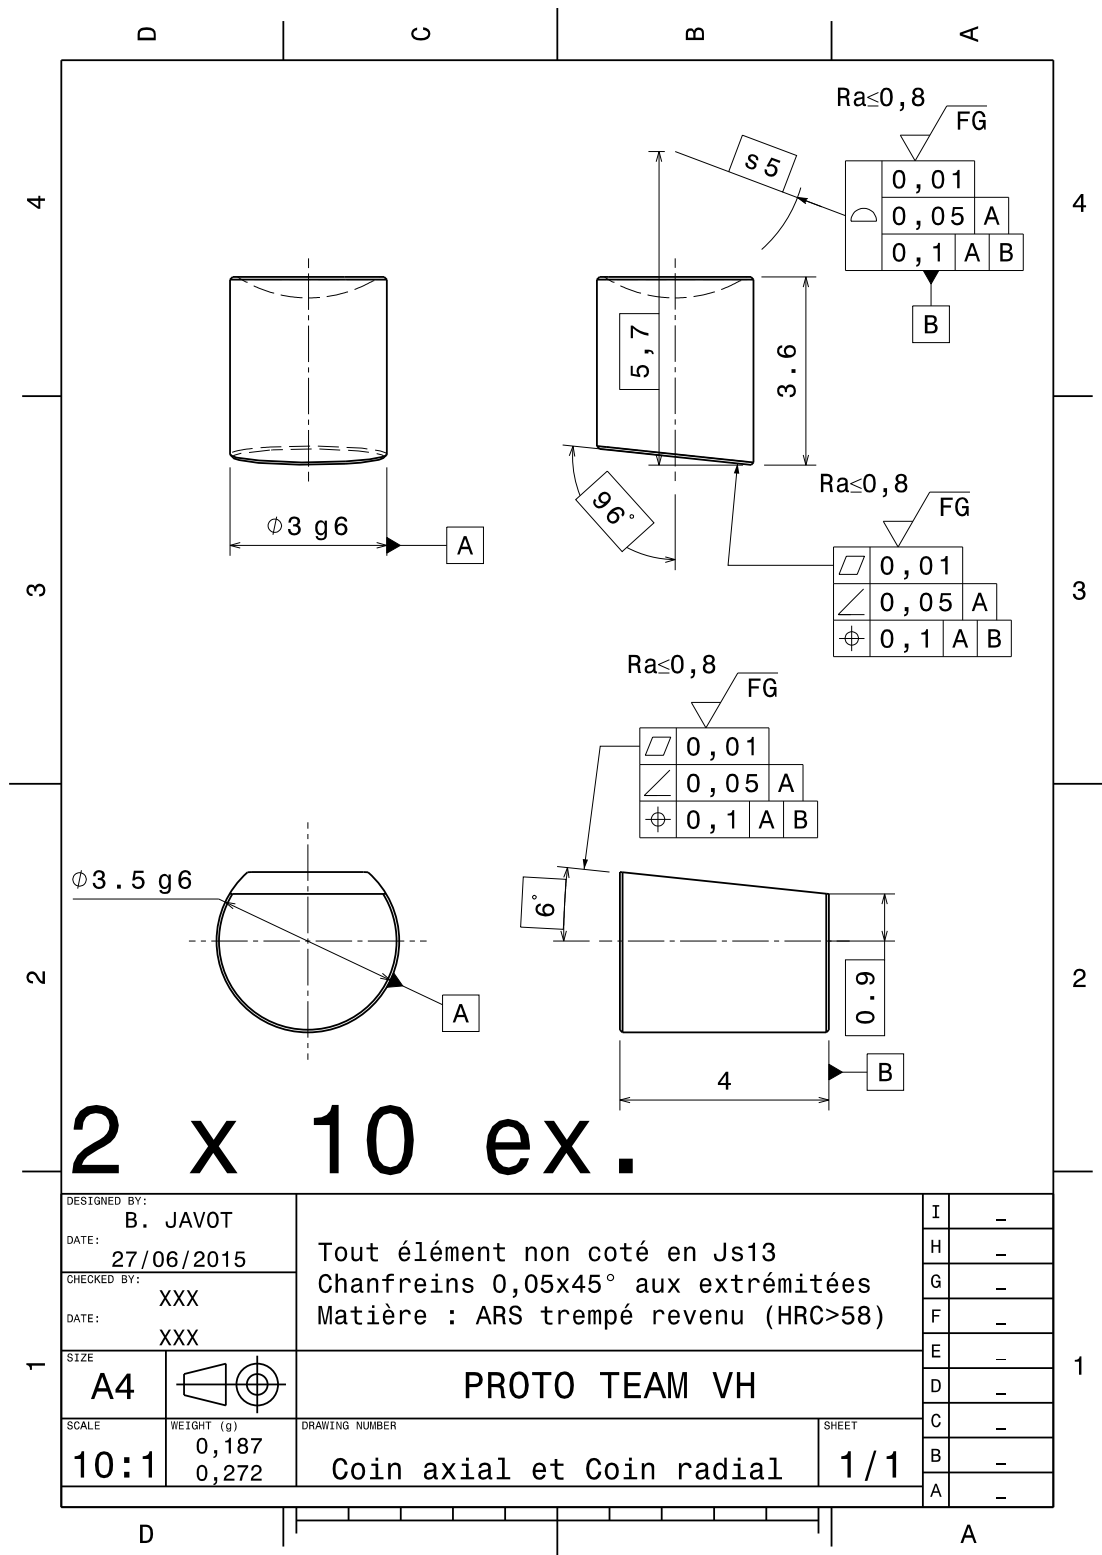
Pièces prototype : Coin axial et Coin radial.
